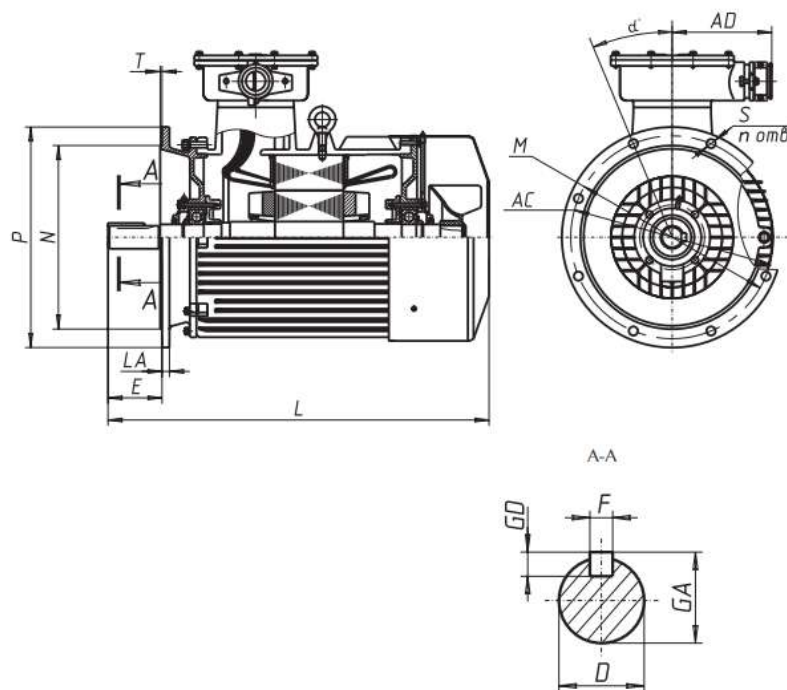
габаритно присоединительные размеры ЭД АИМУ 315 280 М2.
